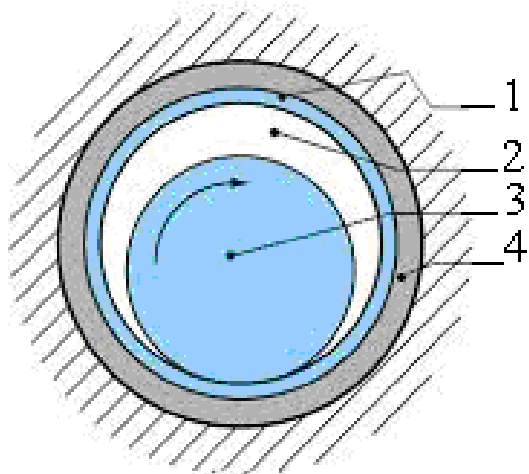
Вальниця ковзання: 1 - вкладиш із антифрикційного матеріалу; 2 - зазор; 3 - вал; 4 - корпус вальниці
